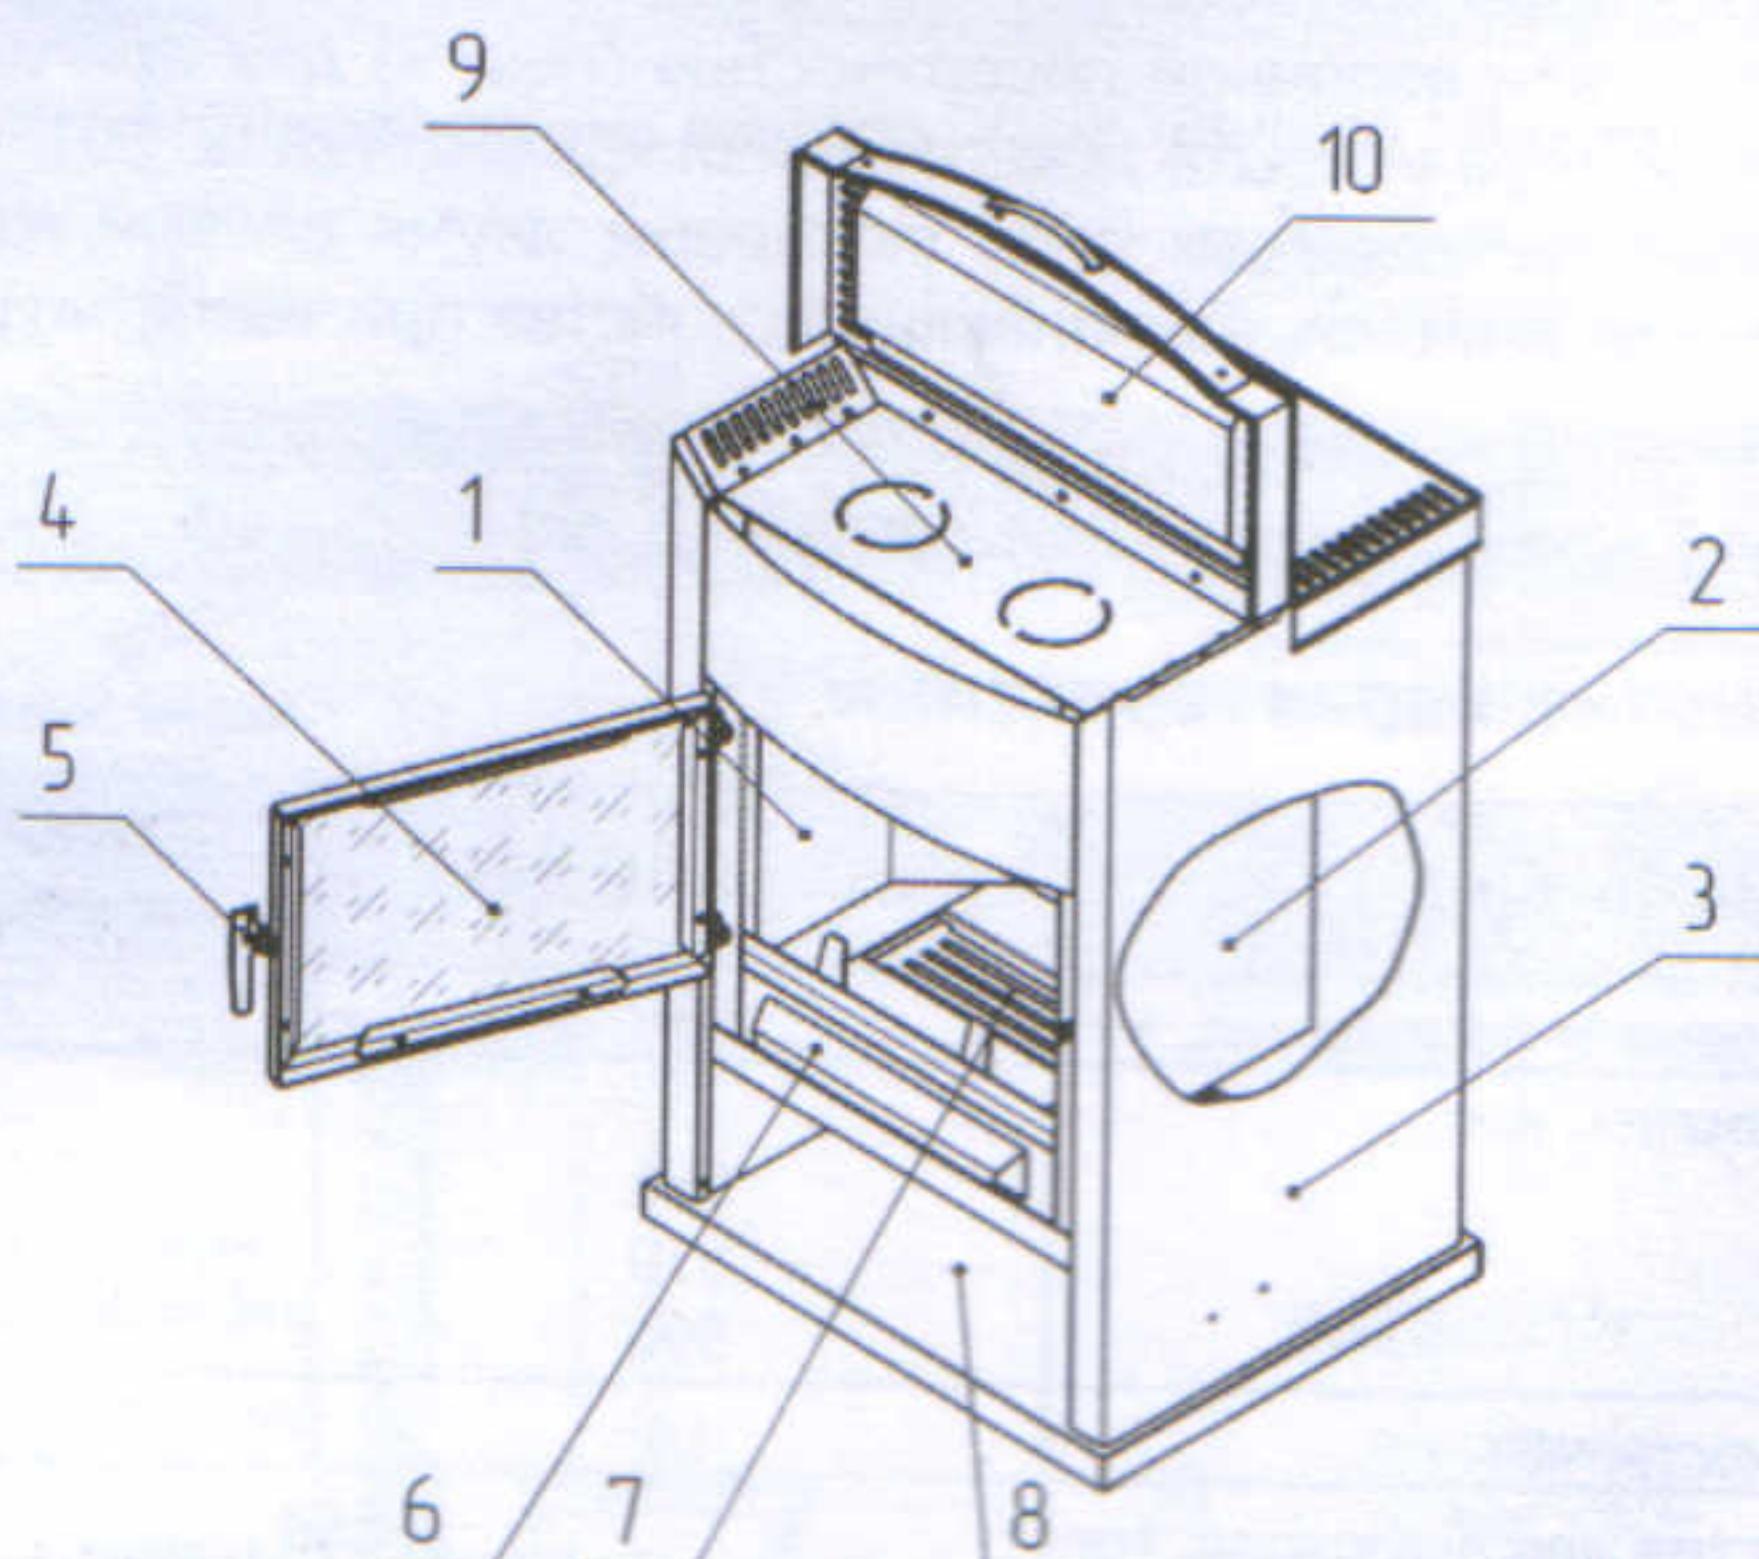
Общий вид камина «ТЕПЛОДАР ОВ-140»
